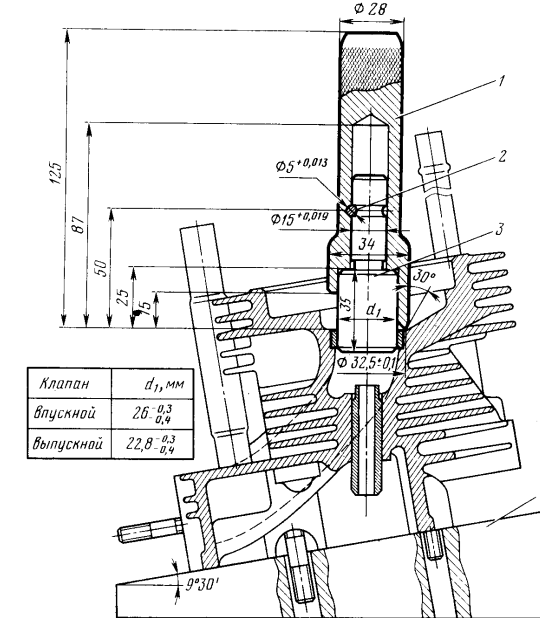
Оправка для зачеканки седла клапана: 1 — корпус; 2 — штифт; 3 — вставка; 4 — подставка
